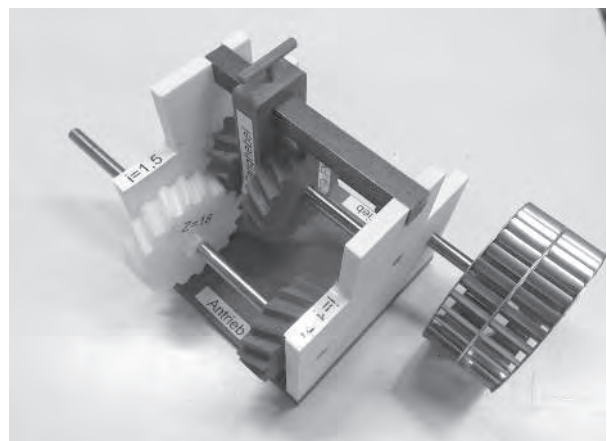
Getriebe mit Komponenten aus dem 3D-Drucker
